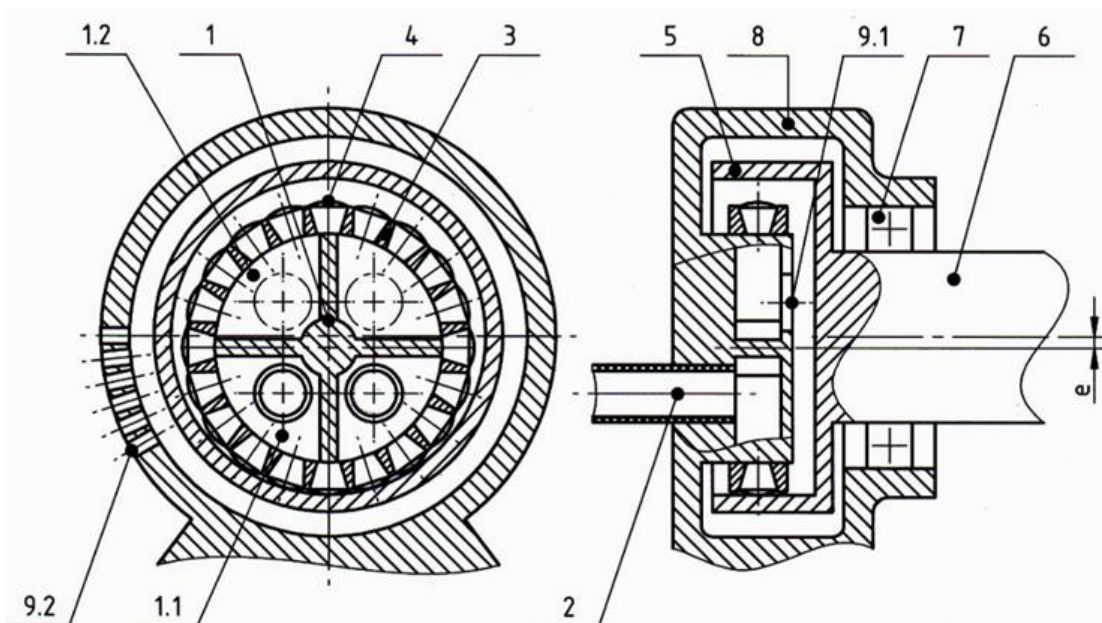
Princip přetlakového pomaluběžného pneumotoru 3
